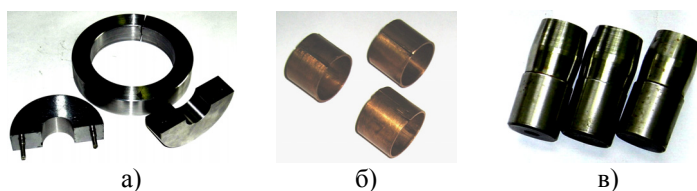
Разъемная обойма (а) заготовка свертной втулки (б), дорны (в)
